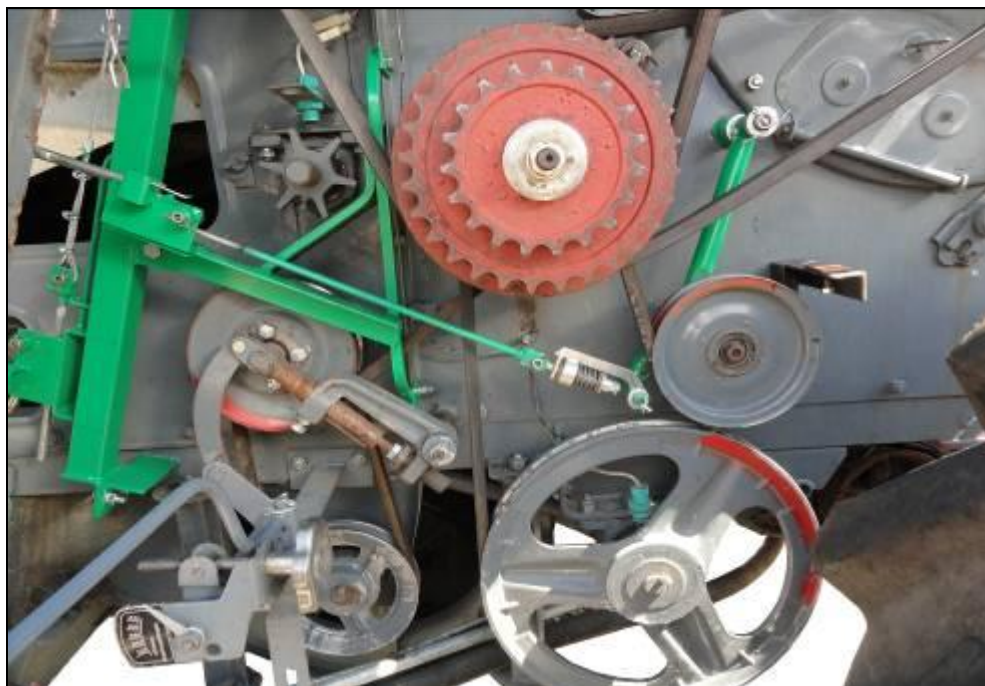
НС-7- натяжник привода от вала главного контрпривода на колебательный вал очистки с комбайна "НИВА", вид сбоку
